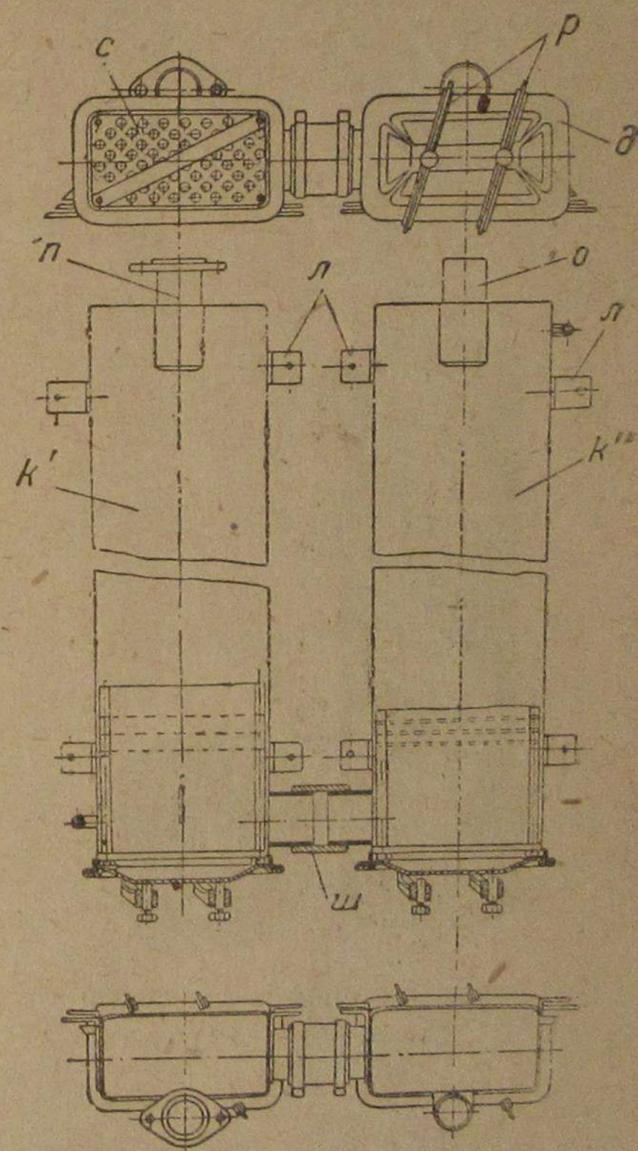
Чертеж охладителя-очистителя машины ГАЗ-АА
